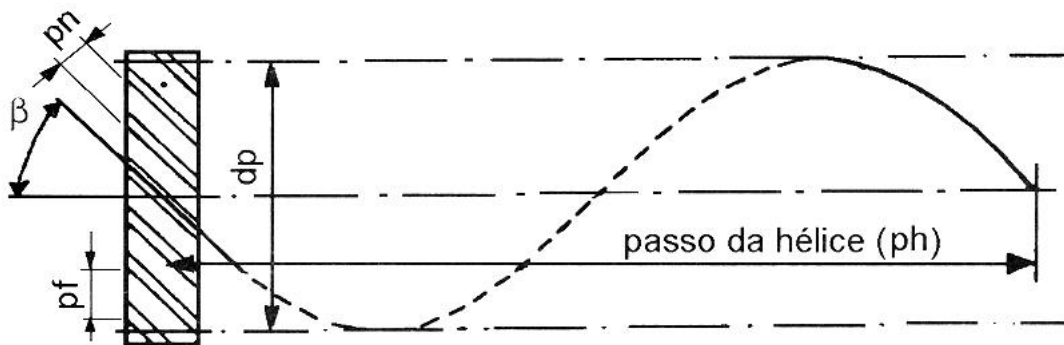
Fresagem de engrenagens de dentes helicoidais.
